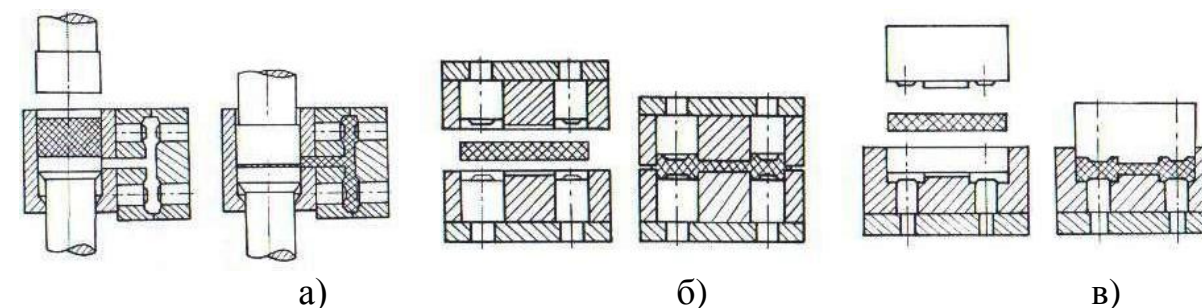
Схема получения изделий шатуна из КАМ различными методами: а – литье под давлением; б – открытая штамповка; в – закрытая штамповка
